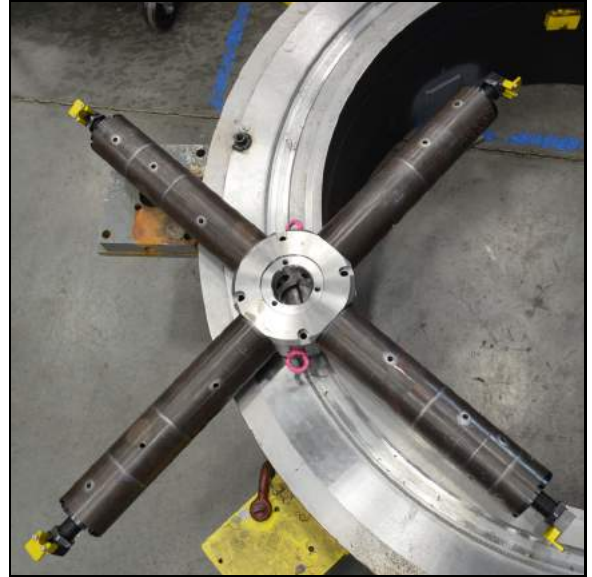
ASSEMBLAGE DU MANDRIN DI
